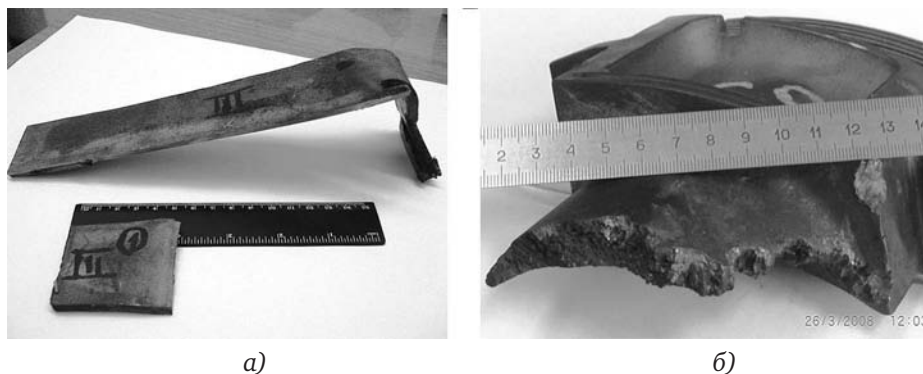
Фрагменты листовой детали (а) и разрушившаяся по перу рабочая лопатка (б) ГТУ
